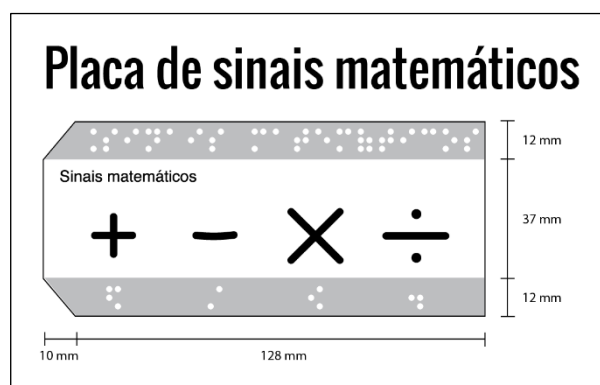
Desenho técnico da placa de sinais matemáticos (fonte: a autora)
